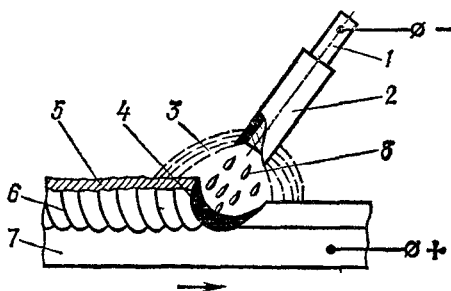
Ручная дуговая сварка металлическим электродом с покрытием (стрелкой указано направление сварки)
